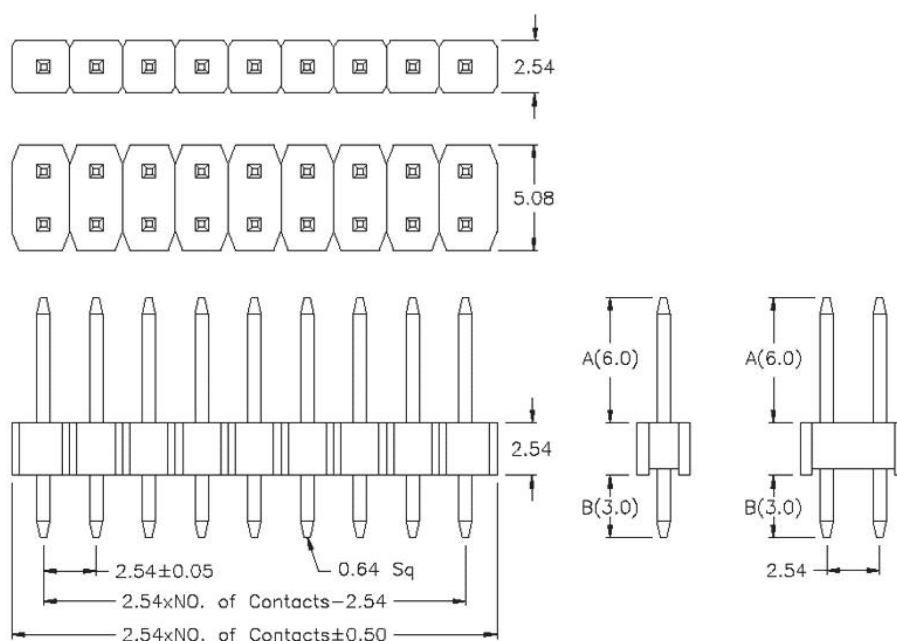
Цоколевка и размеры штыревой вилки
